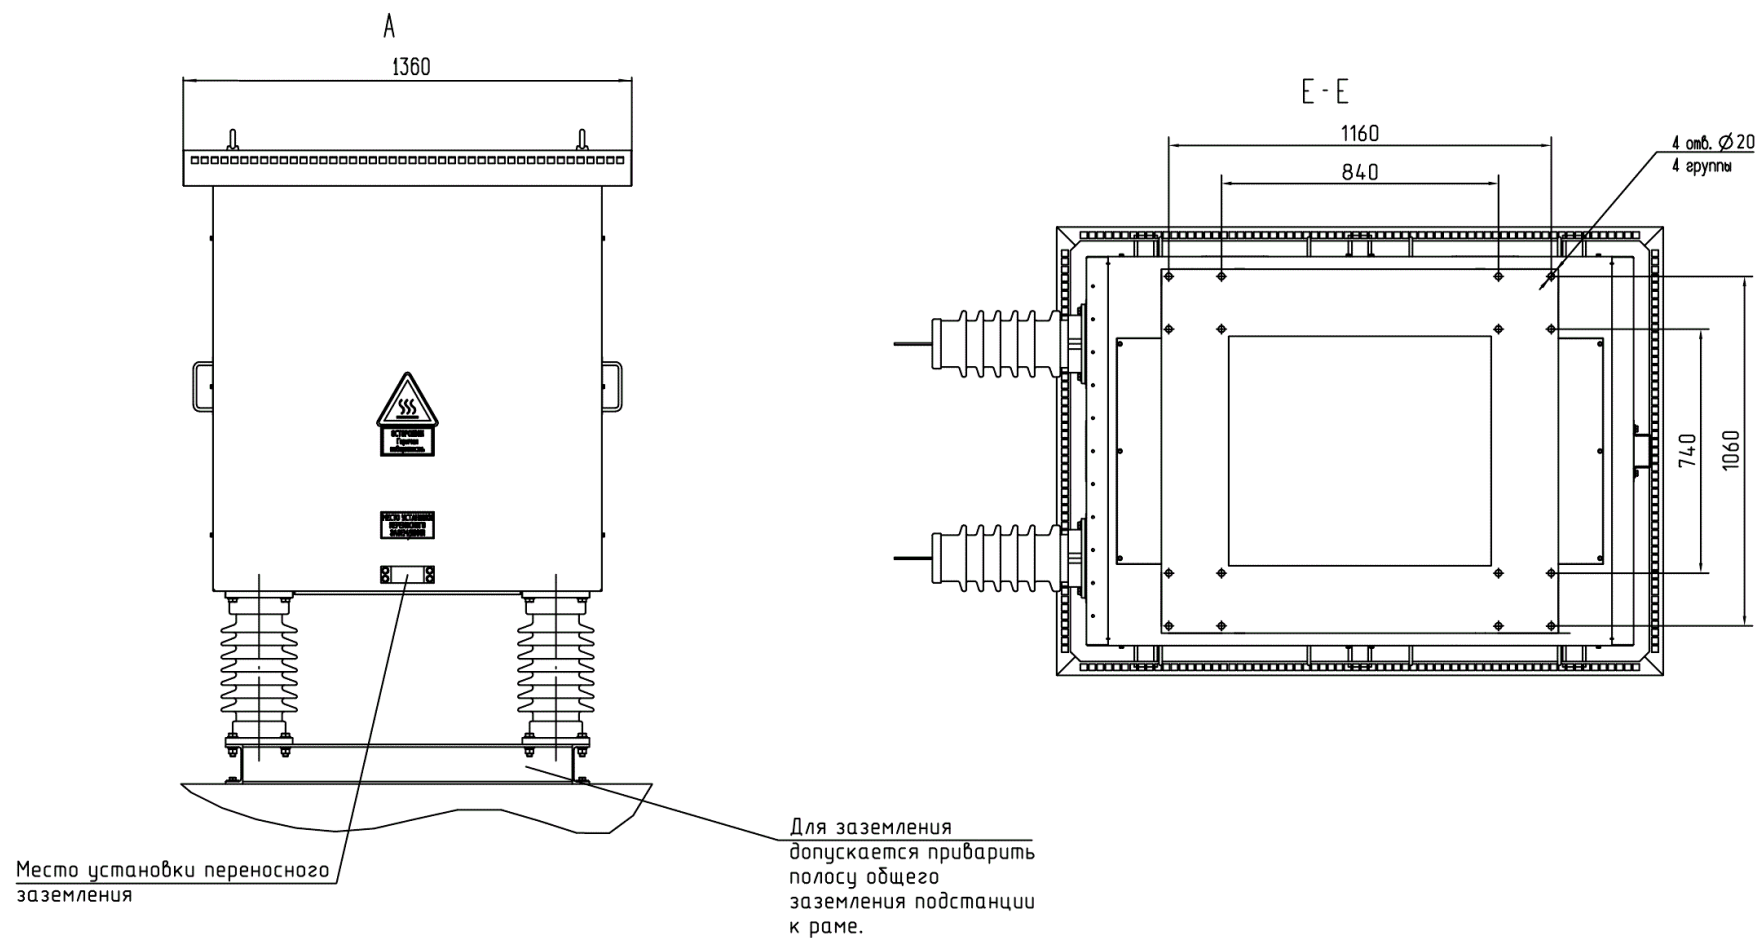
Габаритный чертеж камеры резисторов фильтра R-C-27,5 кВ
